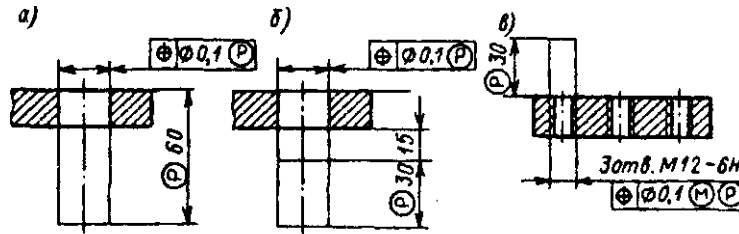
Нанесение выступающего поля допуска расположения
